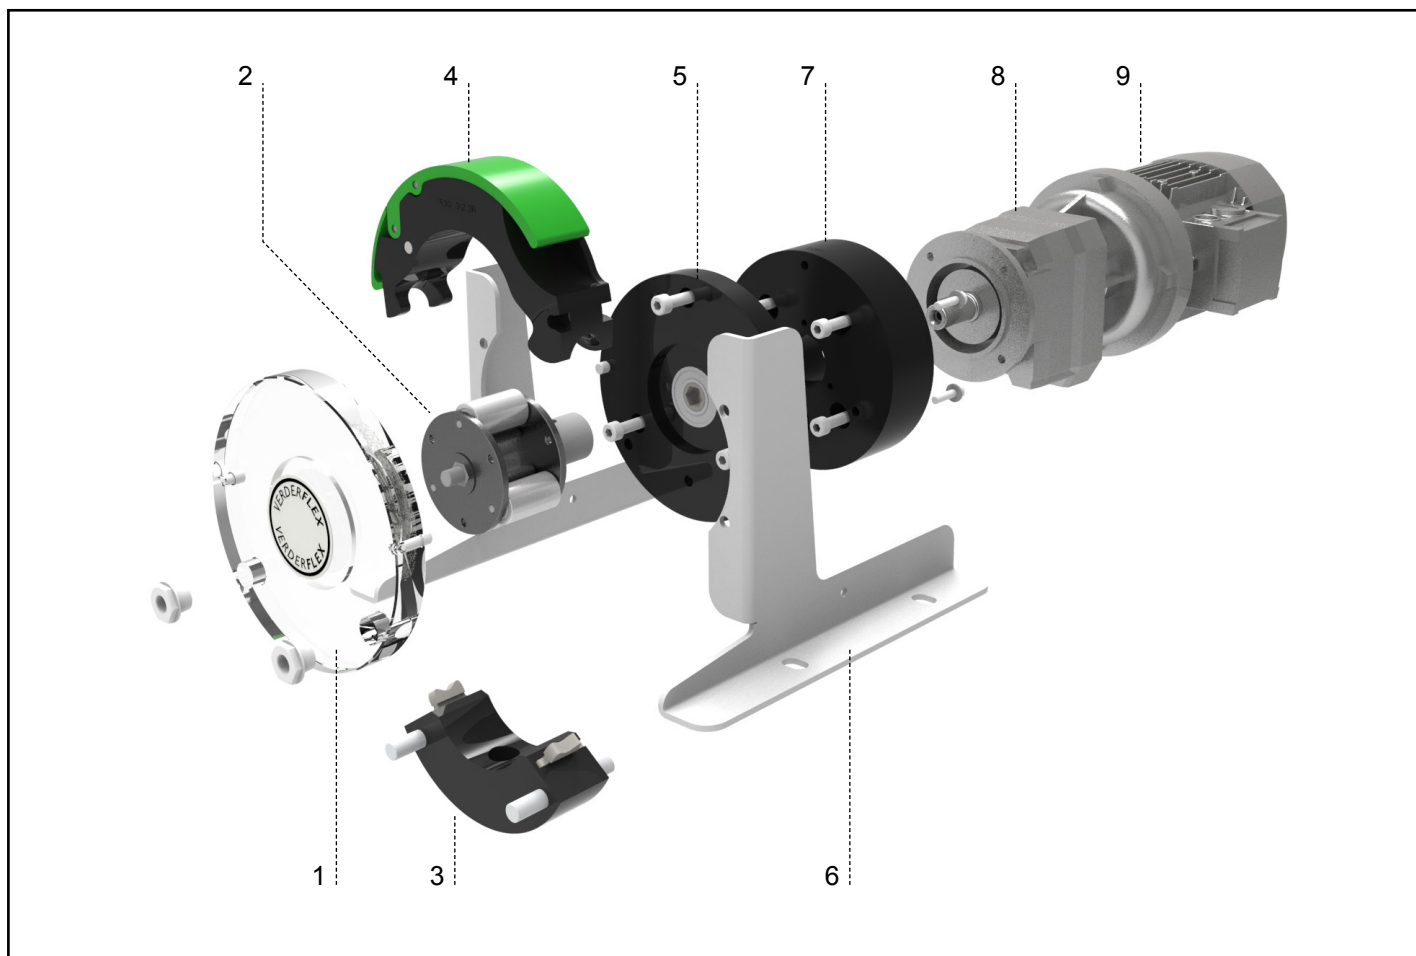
Сборочный чертеж – Rapide ‘S’
